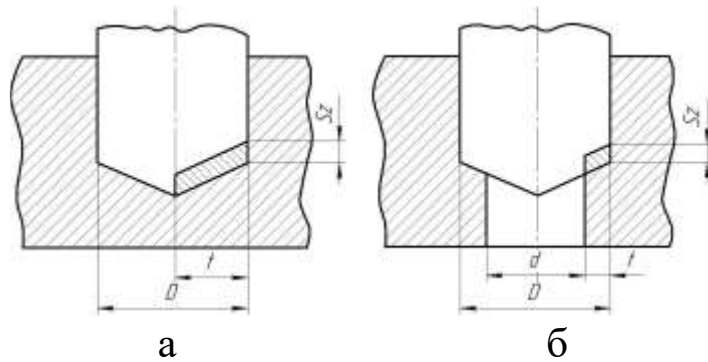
Схеми для визначення глибини різання при свердлильних видах обробки
